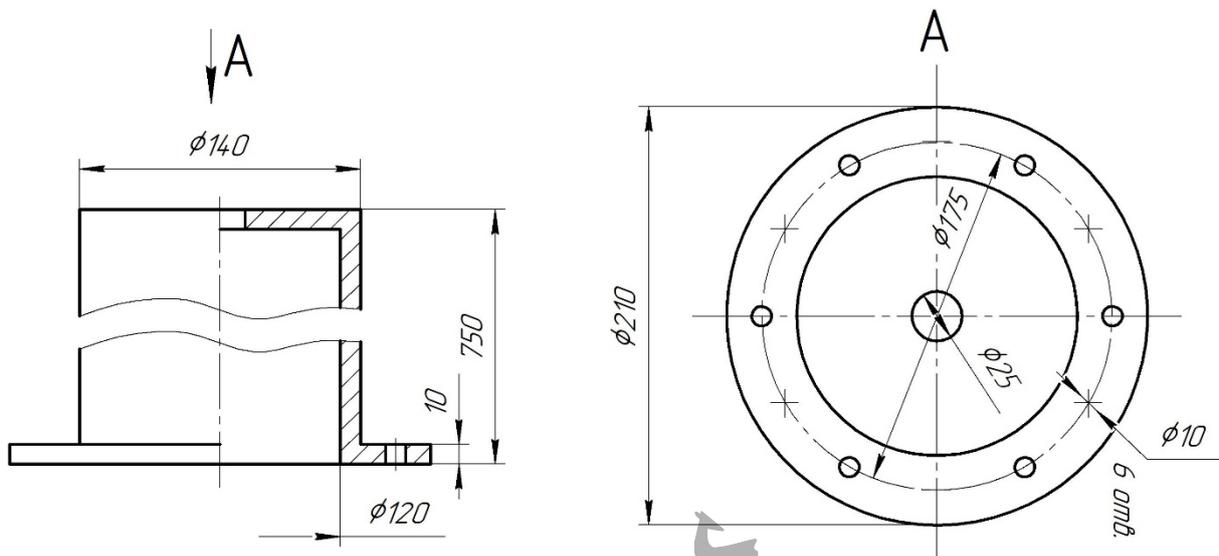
Чертеж корпуса шток-рейки корпуса ОПУ
